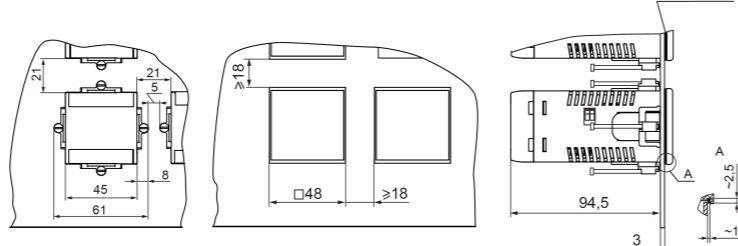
Прибор в корпусе Щ5, установленный в щит толщиной 3 мм
